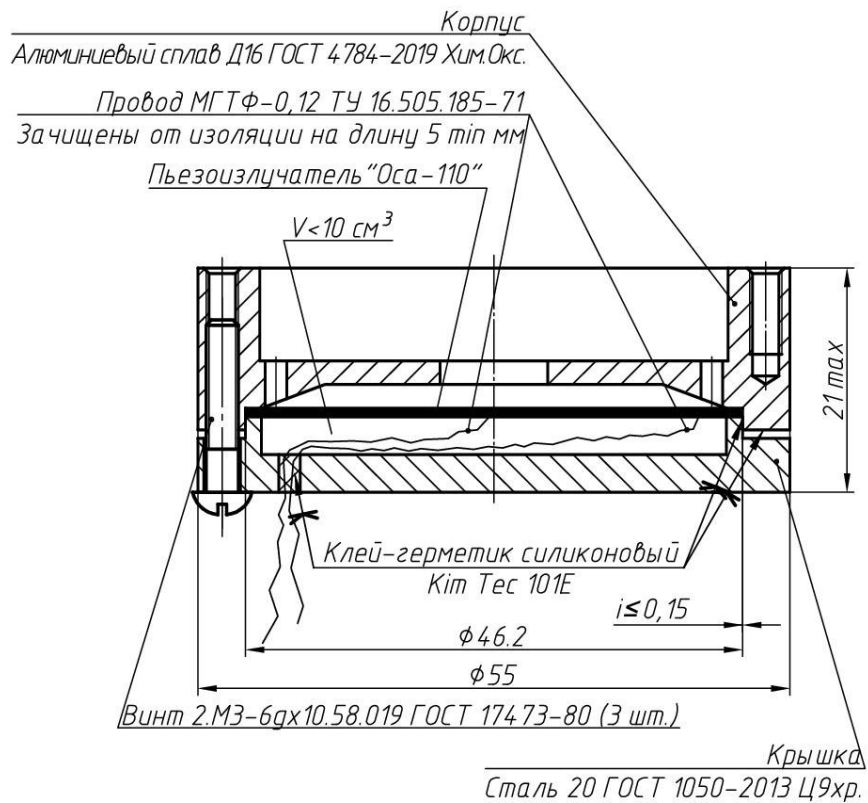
Звуковой излучатель для оповещателей Филин-1 и Филин-2
